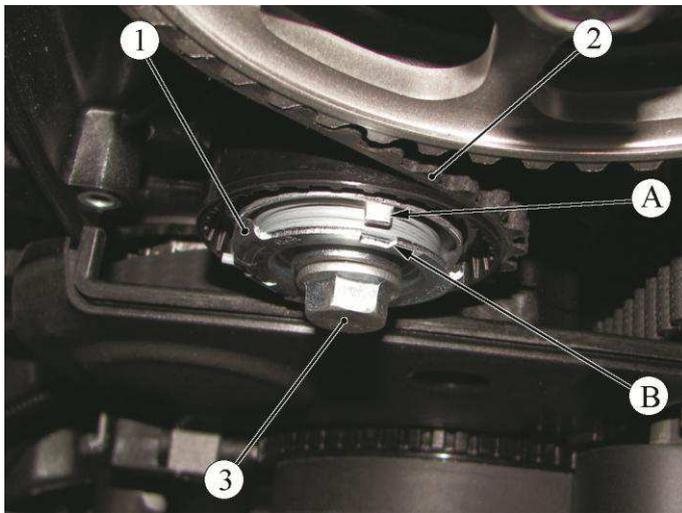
Натяжение ремня привода ГРМ двигателей 11186 и 21116:
